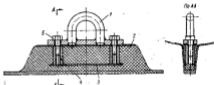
Конструкция крепления рамы к корпусу спасательной шлюпки.
